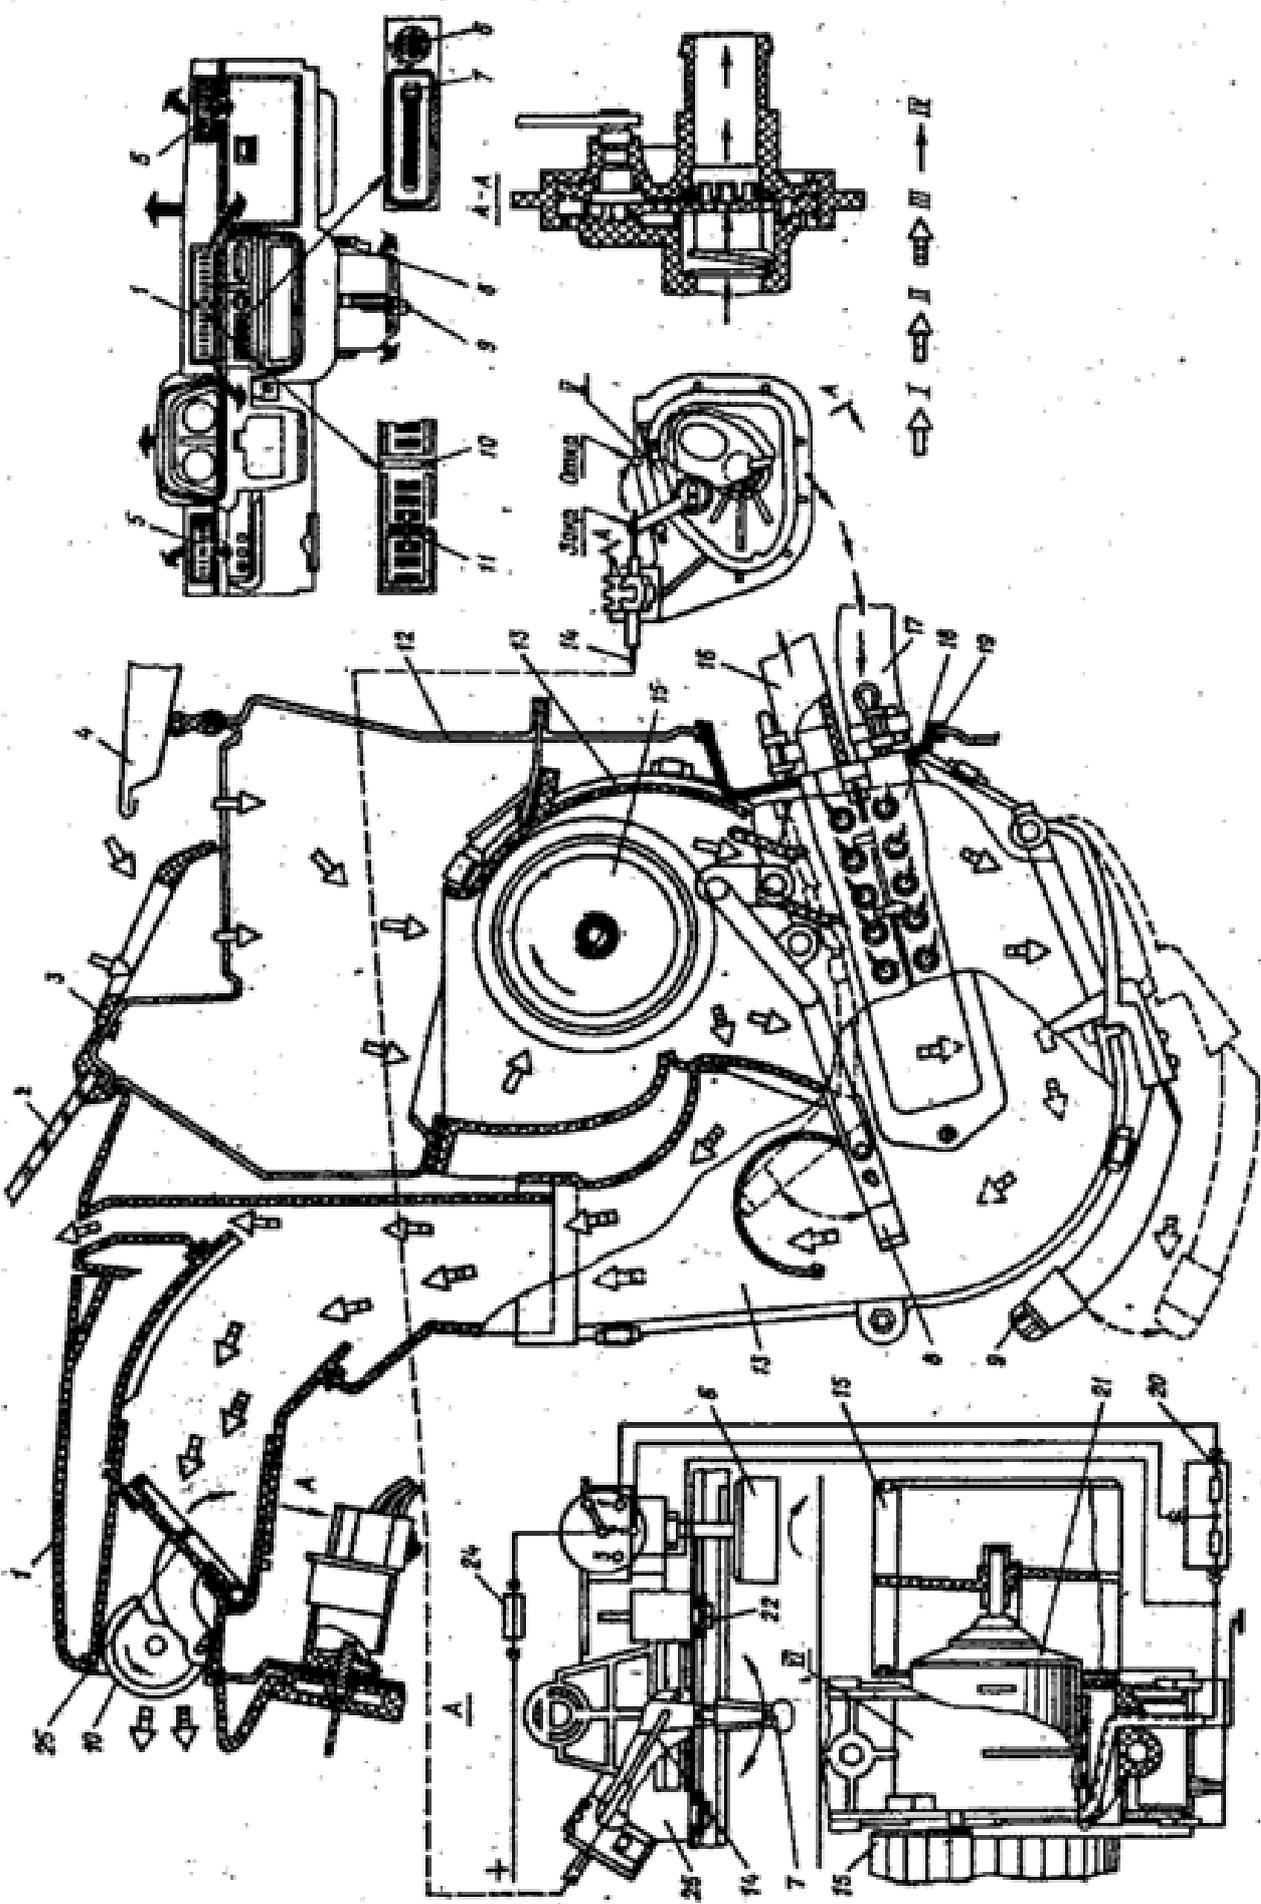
Отопление и вентиляция: 1 - панель приборов; 2 - стекло ветрового окна; 3 - облицовка панели; 4 - капот передка; 5 - боковые сопла системы отопления и вентиляции салона; 6 - ручка переключения частоты вращения электродвигателя вентилятора; 7 - рукоятка управления краном отопителя; 8 - рычаг управления заслонками отопителя; 9 - рычаг открытия нижней заслонки; 10 - ручка (маховичок) привода заслонки; 11 - рукоятка управления направляющими сопел; 12 - панель воздухопритока; 13 - кожух отопителя; 14 - тяга управления краном отопителя; 15 - колесо рабочее; 16 - шланг отводящий; 17 - шланг подводящий; 18 - радиатор отопителя; 19 - уплотнитель; 20 - блок резисторов; 21 - электродвигатель вентилятора; 22 - блок крепления блока управления отопителем; 23 - блок управления отопителем; 24 - предохранитель; 25 - заслонка вентиляции центральная; I - путь холодного воздуха; II - путь нагретого воздуха; III - путь воздуха при включении; IV - путь жидкости через кран и радиатор отопителя; V - кран управления; VI - электродвигатель с рабочими колесами и электрическая схема включения; закр. - закрыто; откр. - открыто.
